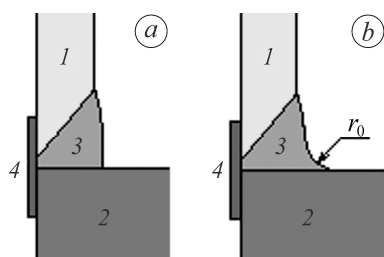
Розрахункова область з'єднання іншого типу: 1 – штуцер, 2 – денце, 3 – зварний шов, 4 – сталеве кільце.
